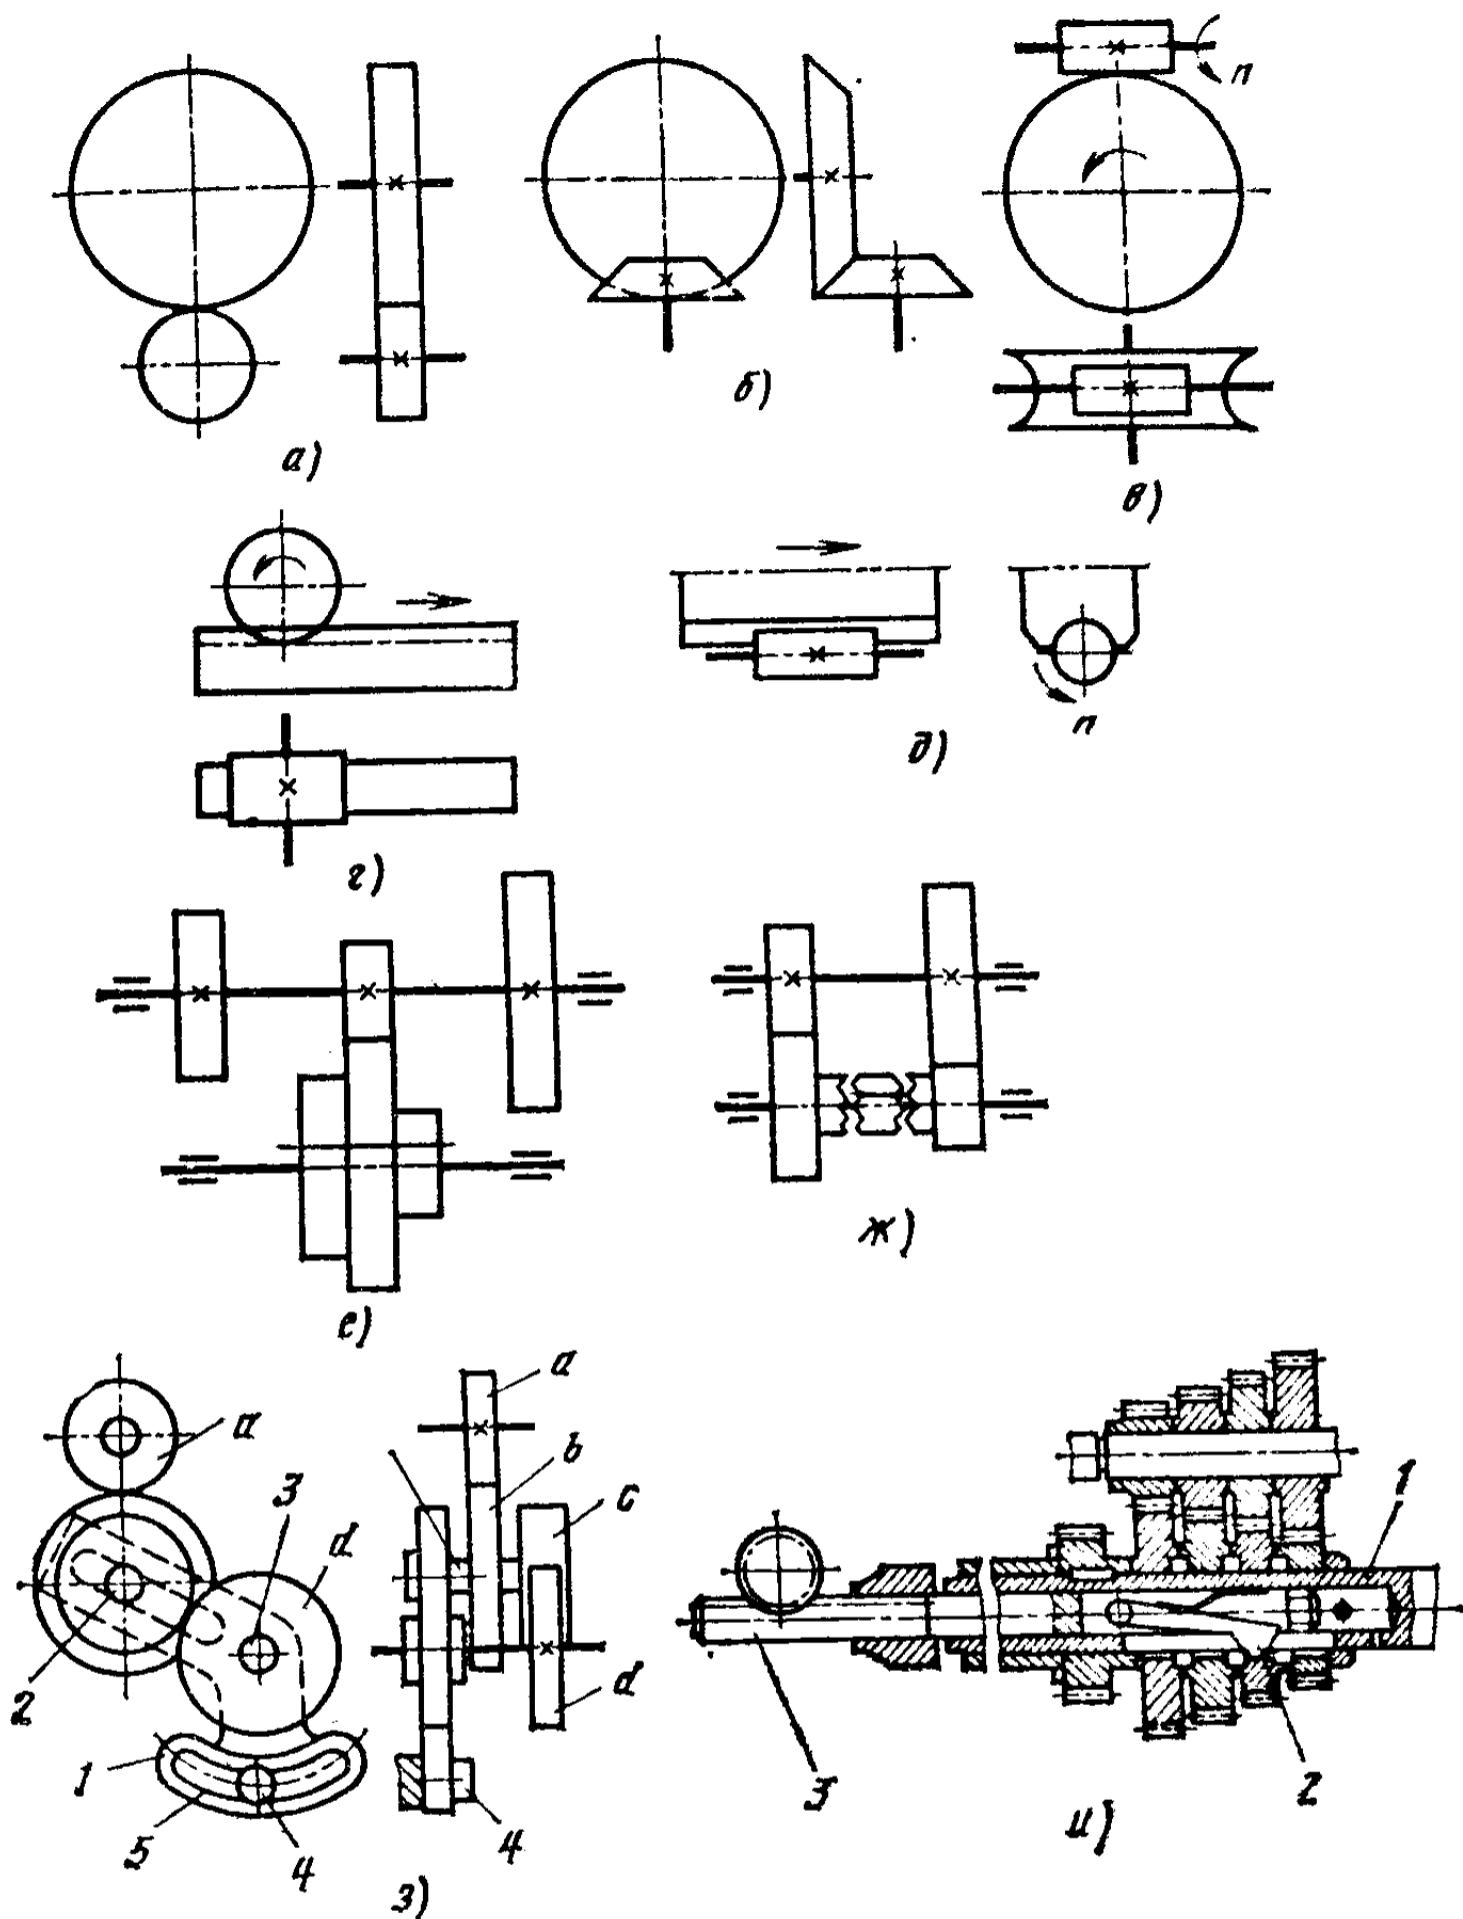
Зубчатые механизмы металлорежущих станков
